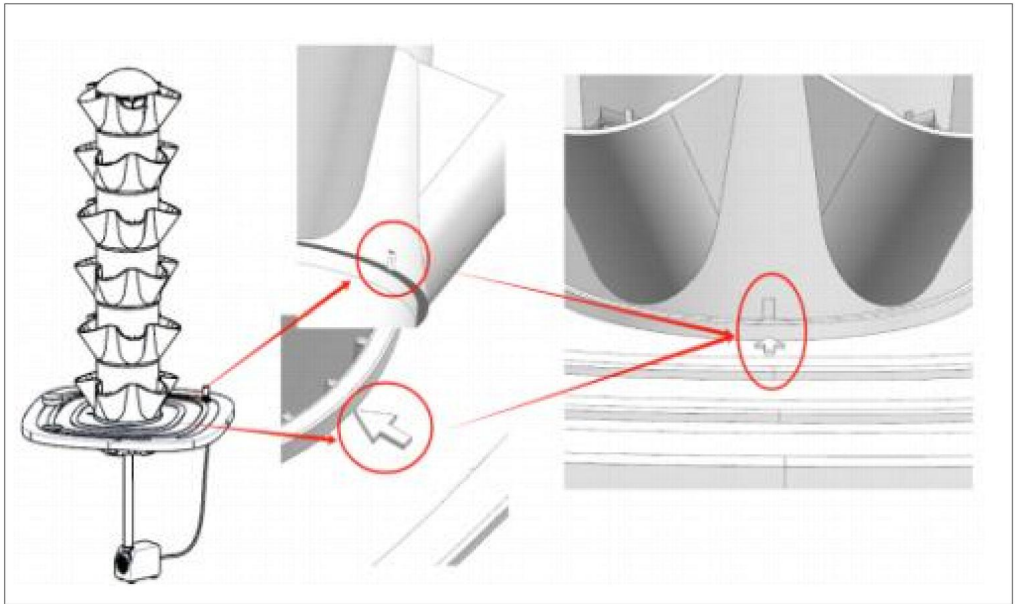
Pase la bomba de agua a través del centro de la tapa del balde como se muestra, posteriormente ensamble la torre de agua en la tapa del balde.
